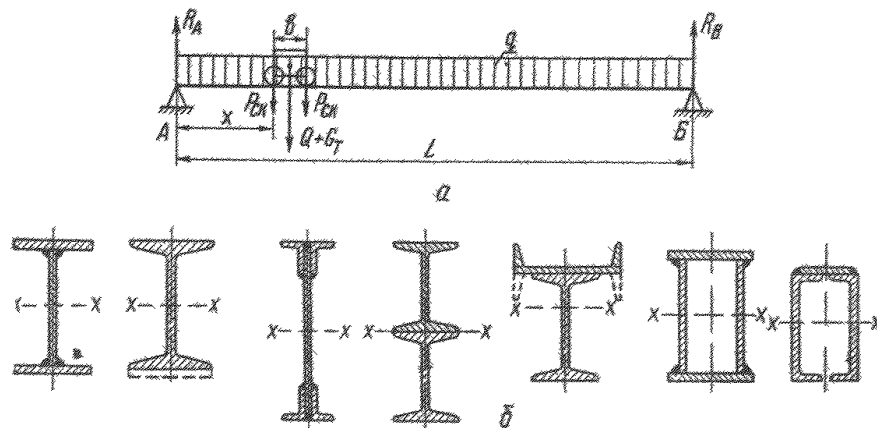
Схема розрахунку балки крана (а); геометричні перерізи балки (б).
